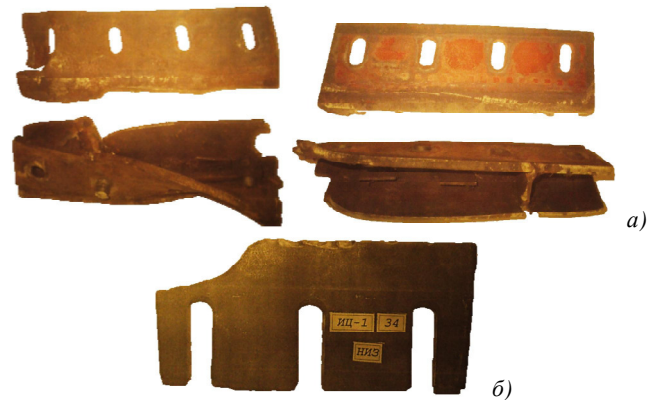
Разрушения стальных элементов (а) измельчающего барабана кормоуборочного комбайна КСК-600 и ножей, изготовленных из чугуна ВЧТГ (б), кормоуборочного комбайна КВК-800
